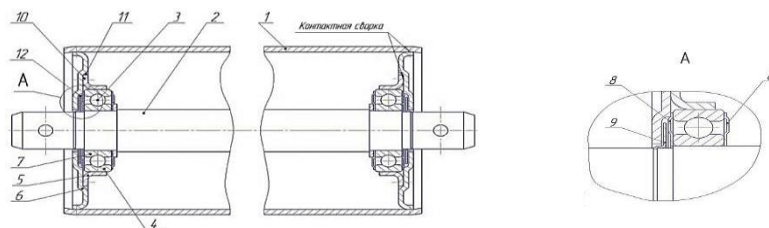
Конструкция разработанного ролика ленточного конвейера
